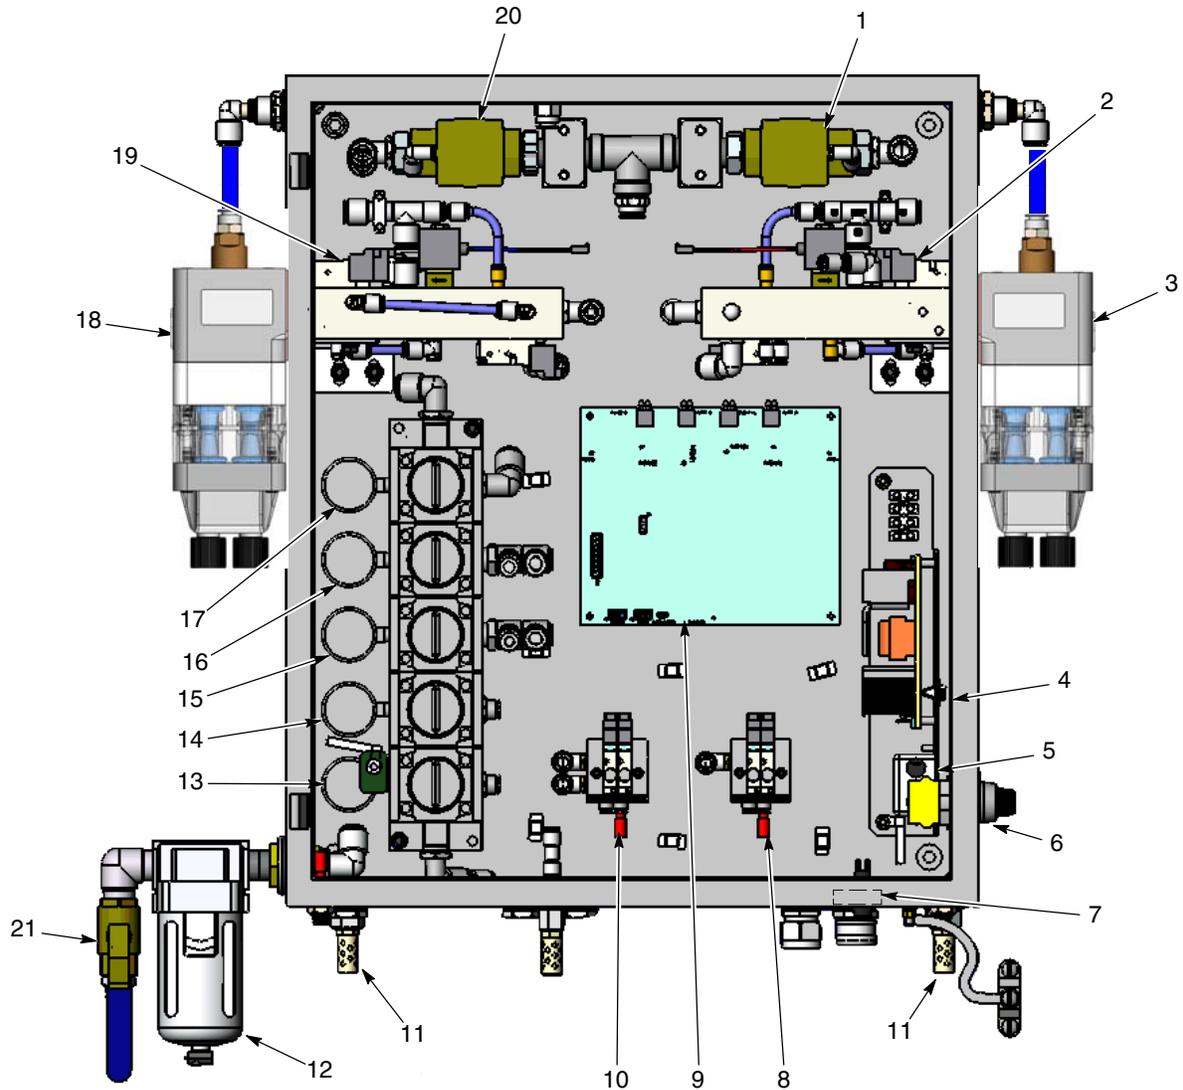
Komponenten der Pumpenkonzole (Abb.: Version mit zwei Pistolen)
